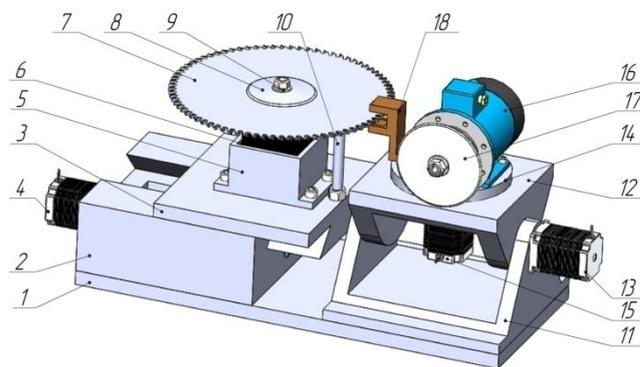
Устройство станка для адаптивной заточки: 1 — плита опорная; 2 — корпус координатного стола; 3 — стол подвижный; 4 — двигатель шаговый с энкодером; 5 — крепление для шагового двигателя; 6 — двигатель шаговый с энкодером; 7 — пила дисковая; 8 — фланец крепежный; 9 — гайка; 10 — кронштейн; 11 — корпус неподвижный; 12 — стол наклонный; 13 — двигатель шаговый с энкодером; 14 — стол поворотный; 15 — двигатель шаговый с энкодером; 16 — шпиндель за-
